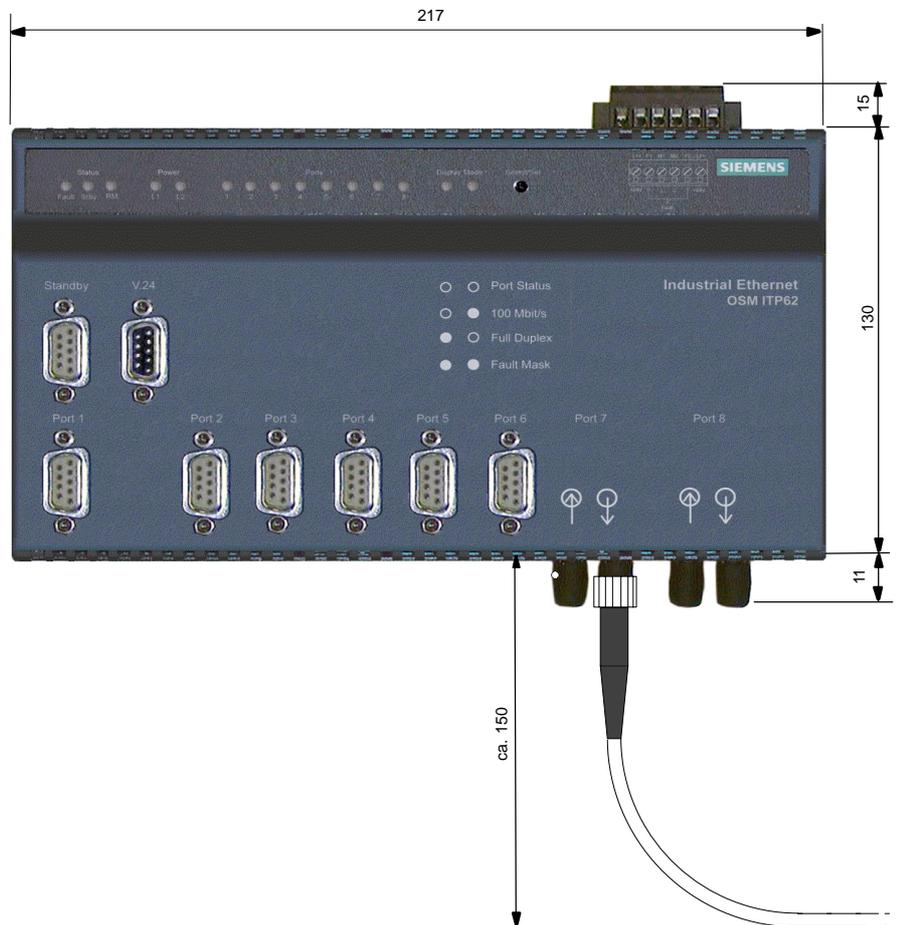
Industrial Ethernet OSM ITPxx (Maße in mm)
